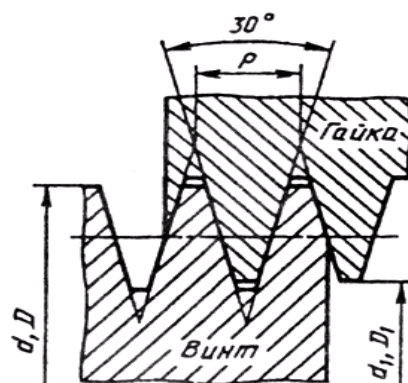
Профиль и основные параметры трапецеидальной резьбы
